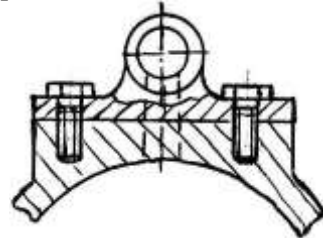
Приклади конструкцій привалочних поверхонь
